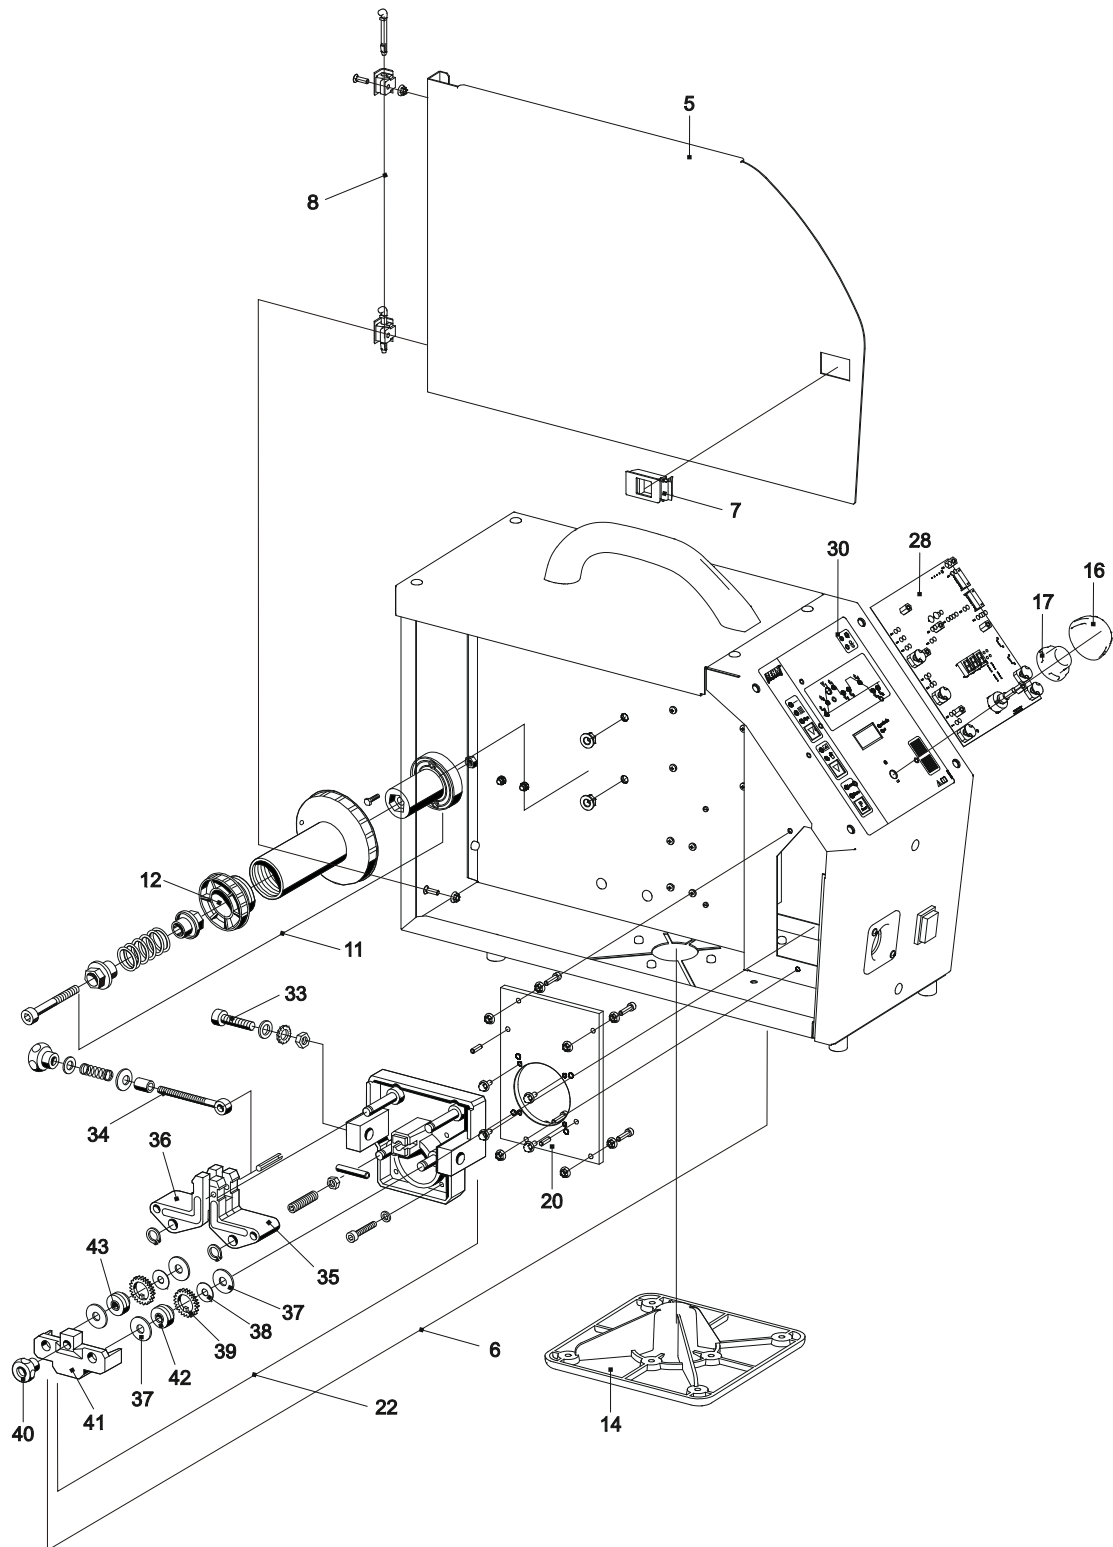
Explosionszeichnung Kaltdrahtgerät APUS 20C
